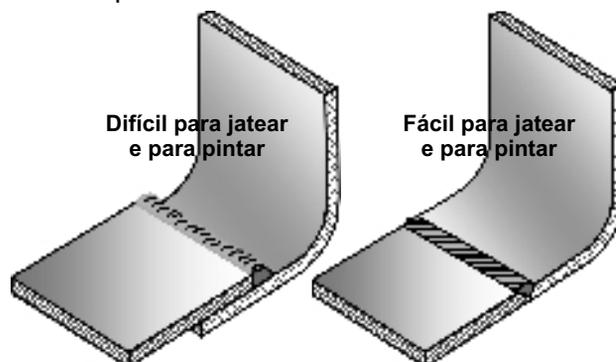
Evitar sobreposições de chapas, preferir soldas do tipo entalhe
